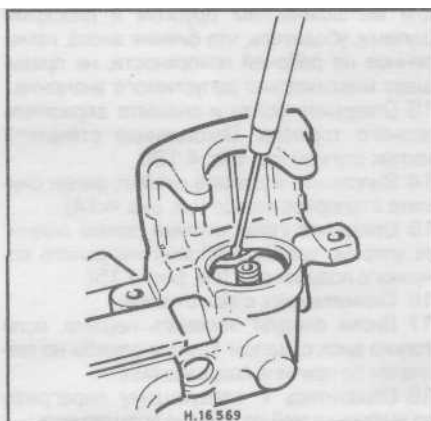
Удаление уплотнительного кольца из цилиндра
